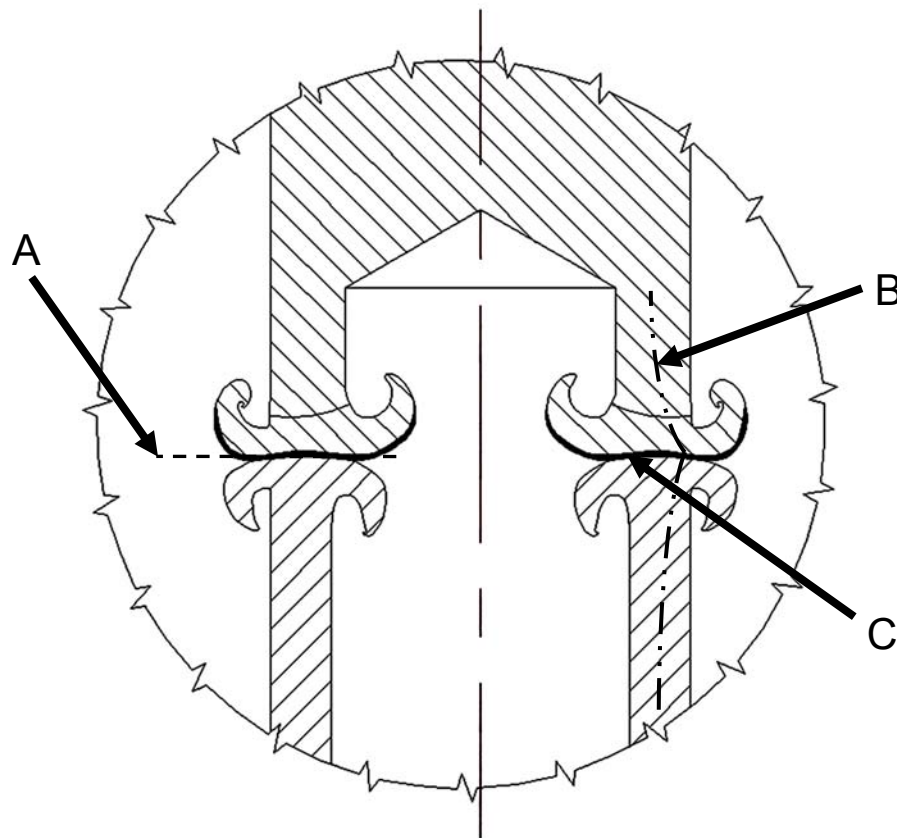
ZB3; Schweißdefinitionen Reibschweißnaht
